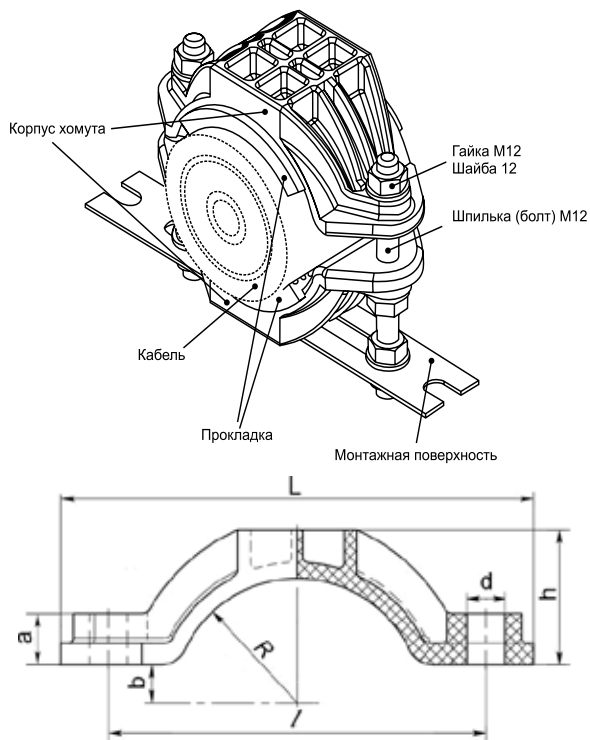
Внешний вид и габаритные размеры (мм)
